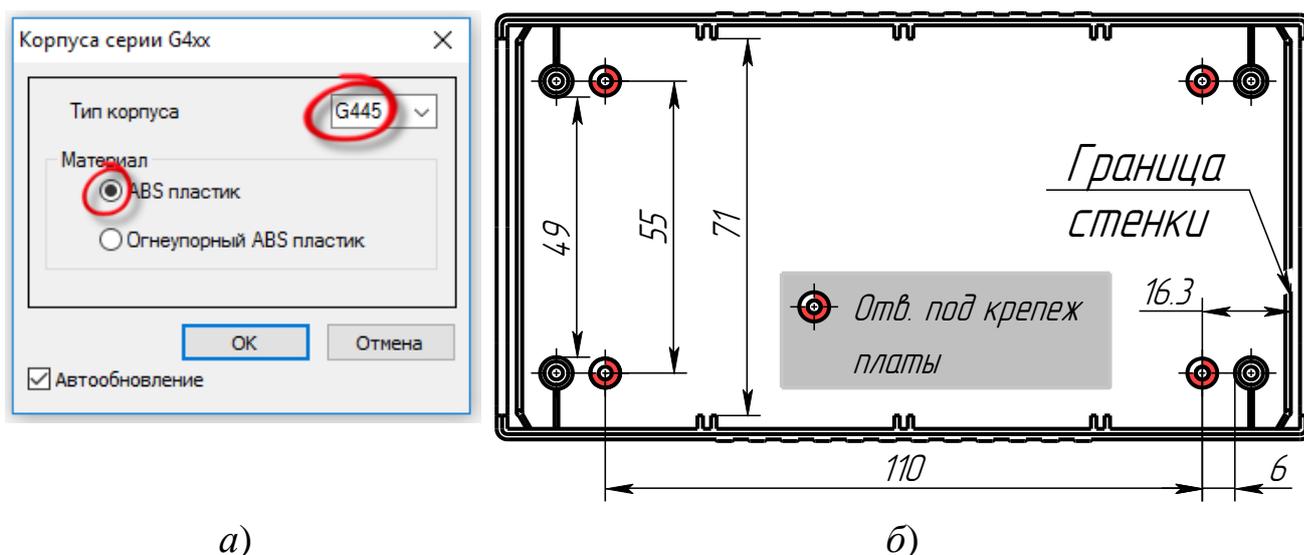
Корпус: а – выбор типоразмера; б – размеры, влияющие на конструкцию печатной платы
